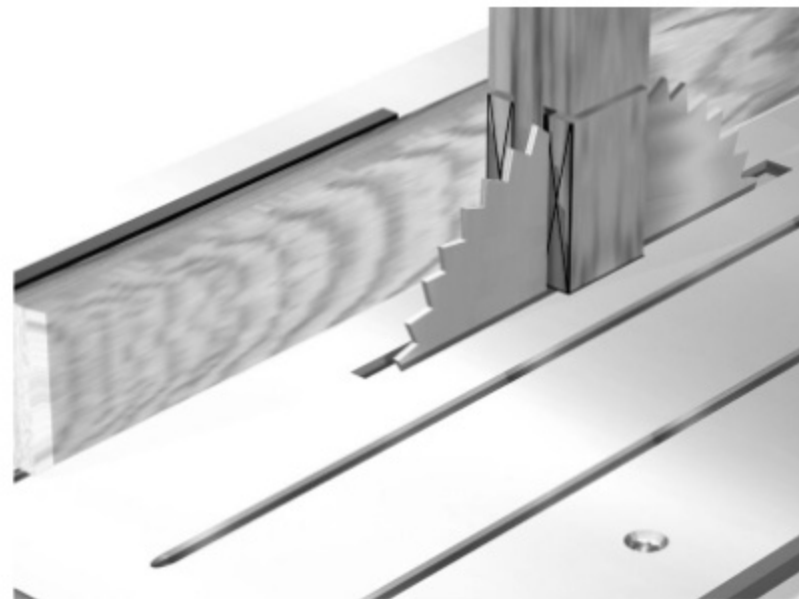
Las espigas se obtienen en el segundo corte con la pieza del asiento en vertical y apoyada en la guía de la mesa
